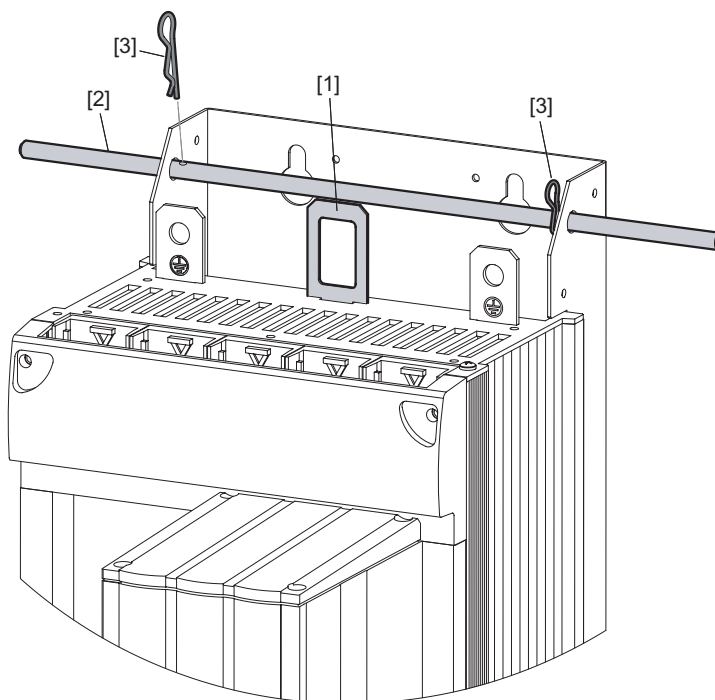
Подъемная проушина и пруток для переноски MOVIDRIVE® типоразмера 6 54406АХХ
